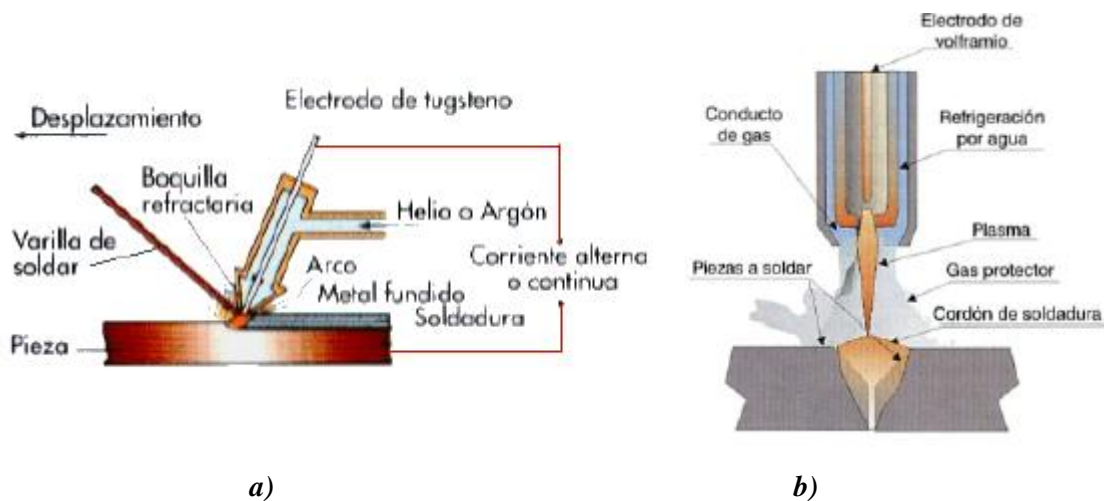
Elementos de la soldadura por arco en atmósfera inerte y con electrodo no consumible o refractario; a) Vista lateral del proceso de soldadura, b) Vista frontal del proceso de soldadura
